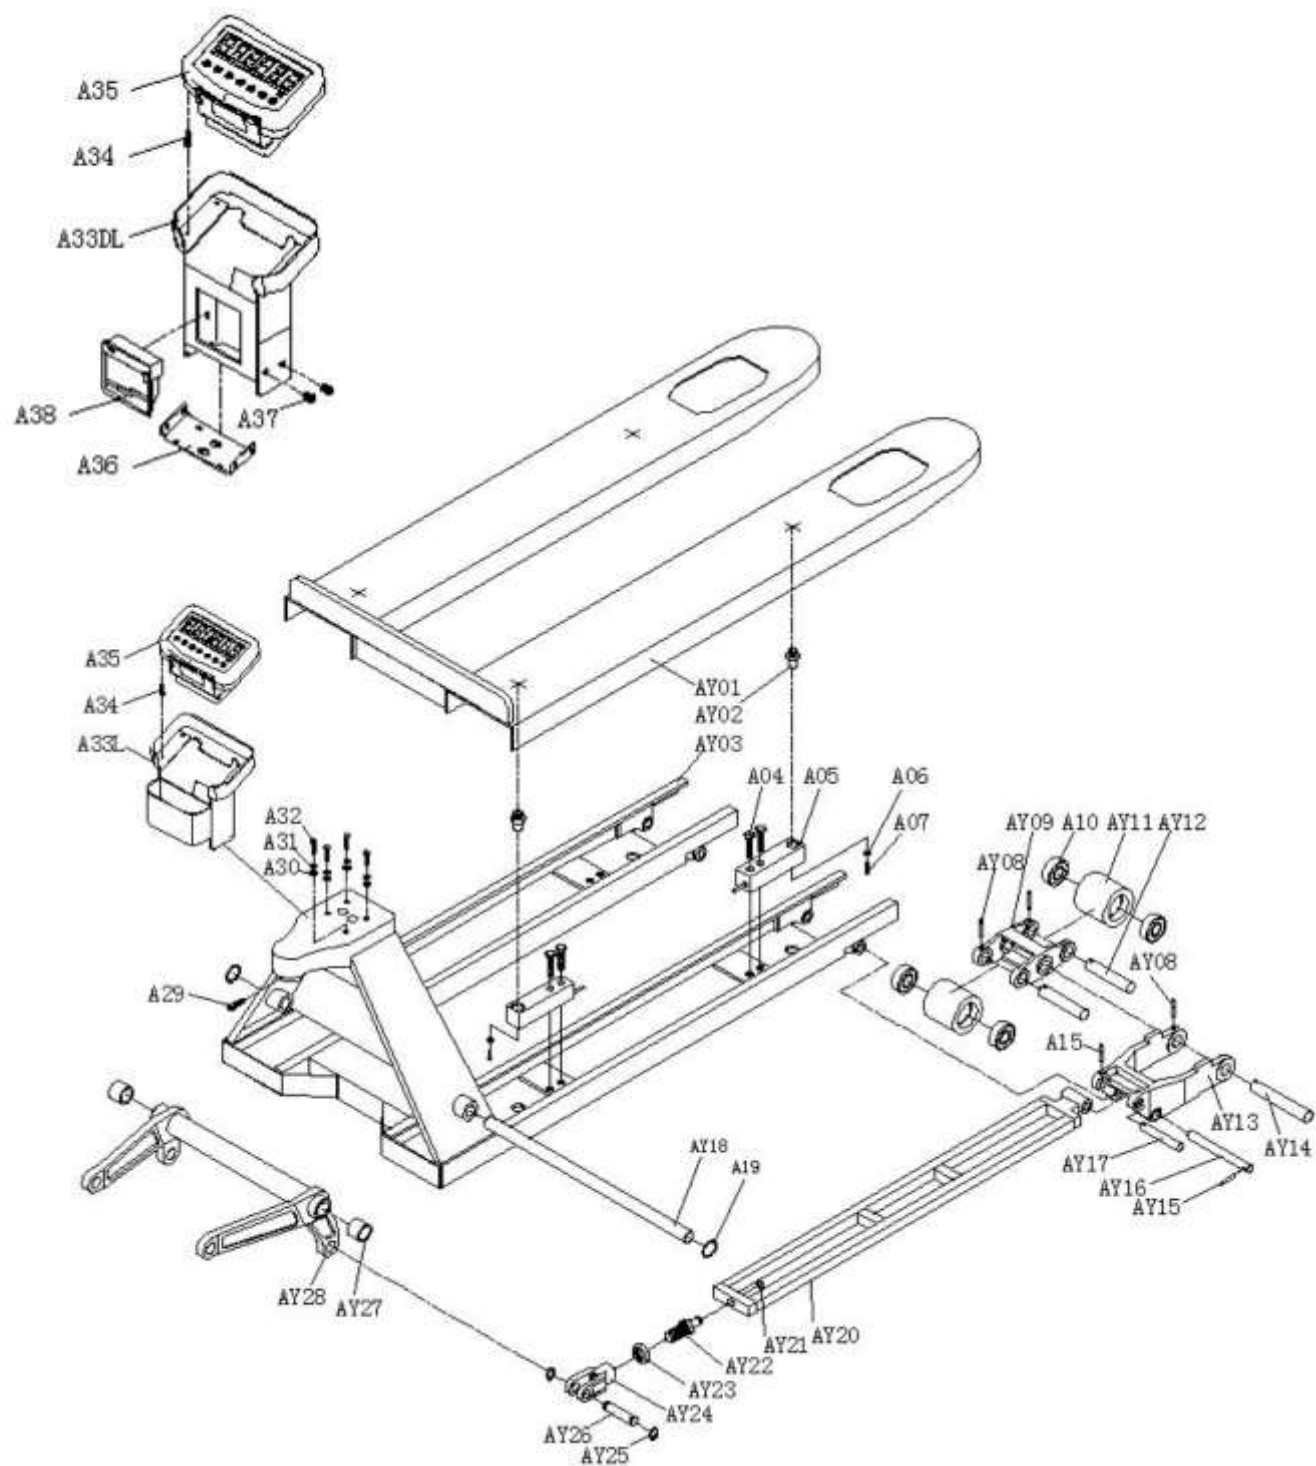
Взрыв-схема корпуса тележки WH-ES.
